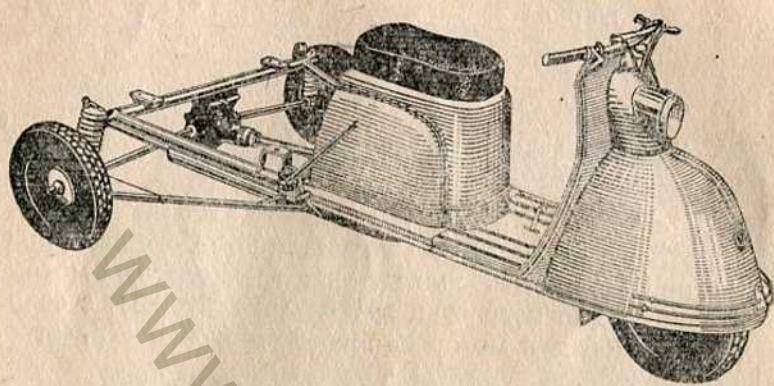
Общий вид шасси грузового мотороллера «Гогго».
